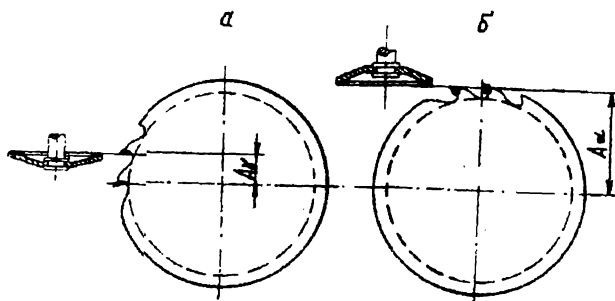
Схема настройки универсально-заточного станка на величину переднего и заднего углов у зубьев пилы
